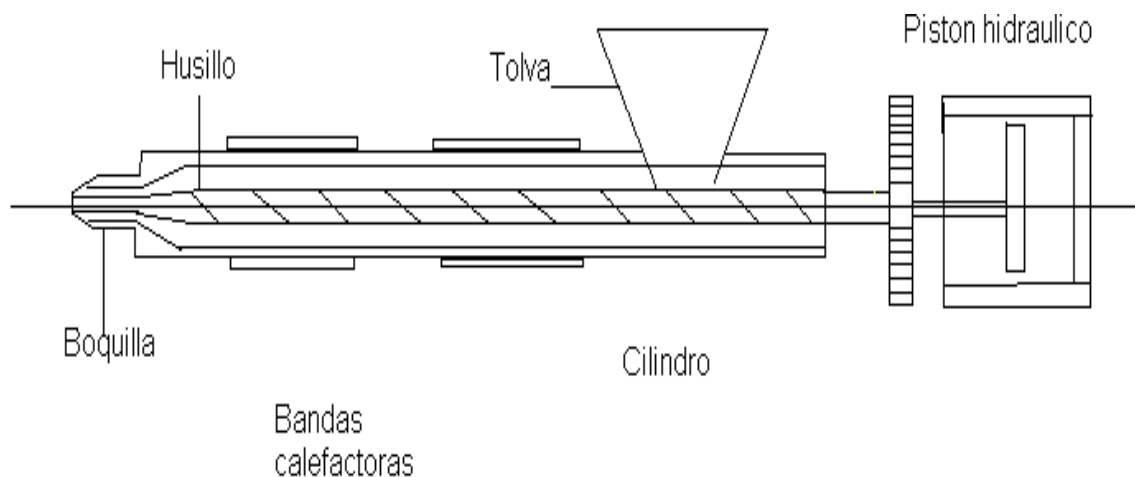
Partes que componen a la unidad de inyección.⁽¹⁰⁾
